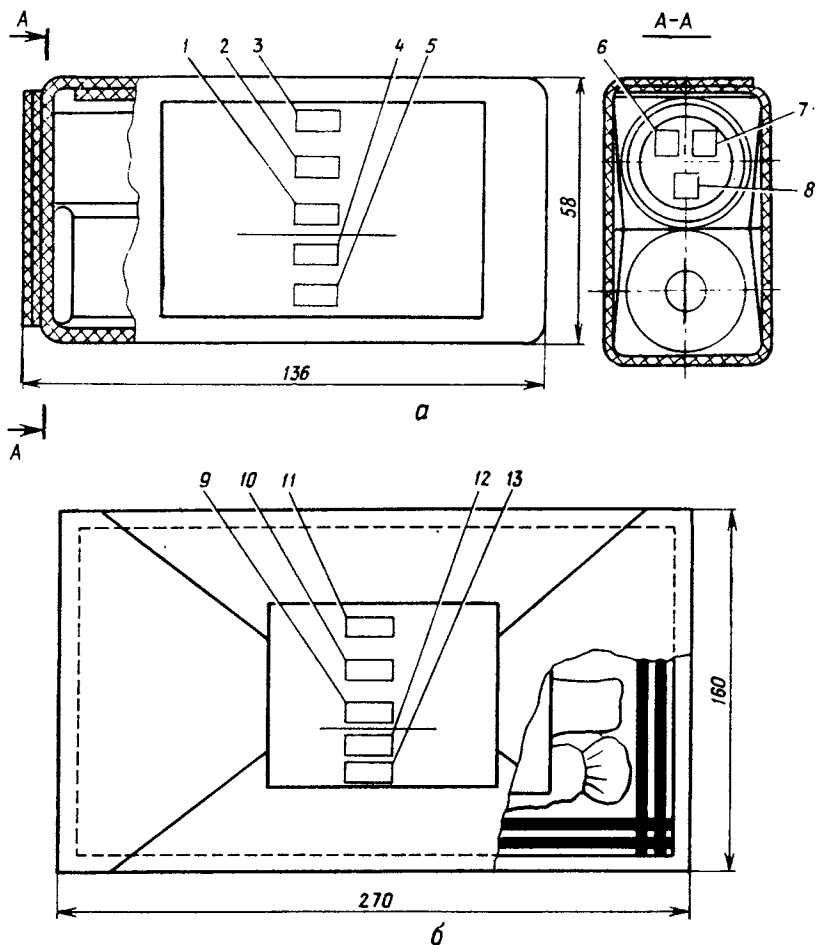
Схема упаковки и маркировки основных метательных зарядов и пакетов:
